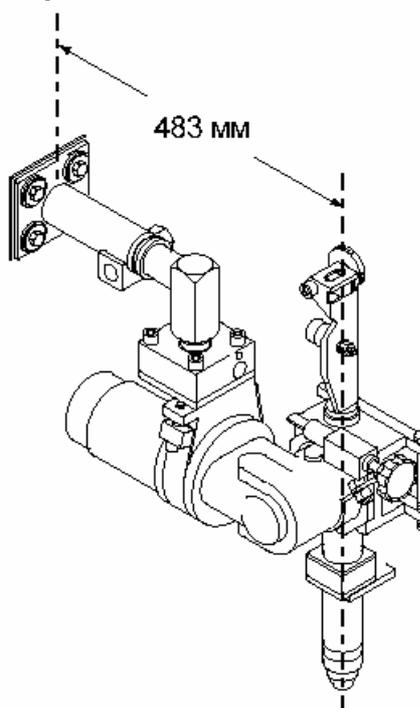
Выравнивание сварочной головки по вертикали
